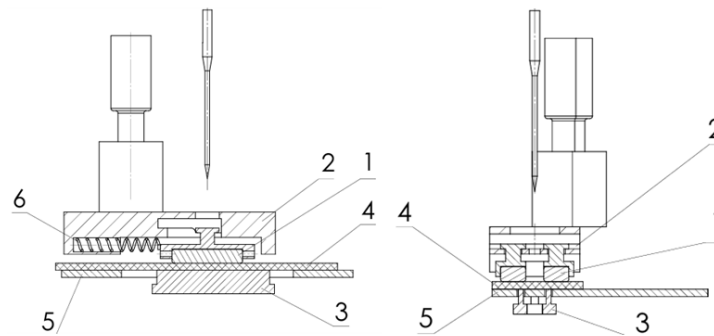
Пристрій переміщення матеріалів: 1 – верхній транспортуючий орган; 2 – корпус; 3 – нижній транспортуючий орган; 4 – матеріал, що транспортується; 5 – голкова пластина; 6 – пружинний елемент
